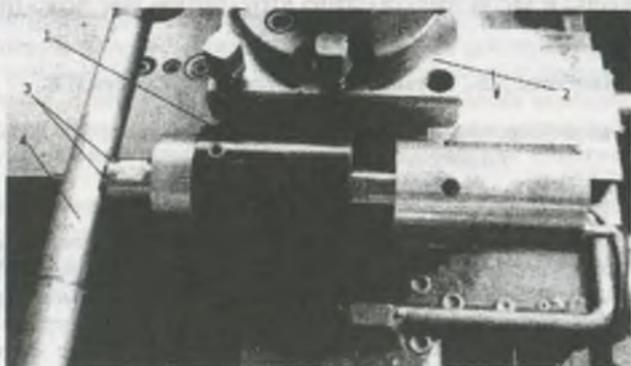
Внешний вид оборудования ультразвуковой упрочняюще-чистой обработки поверхности вала
